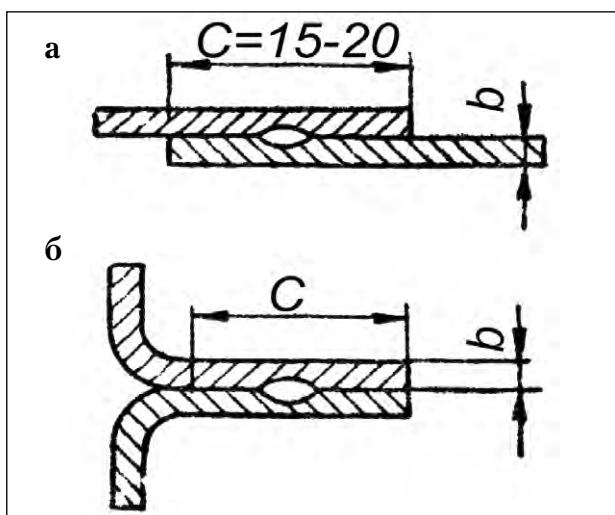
Основные типовые соединения при шовной сварке алюминия и его сплавов: а – внахлестку, б – бортовое
